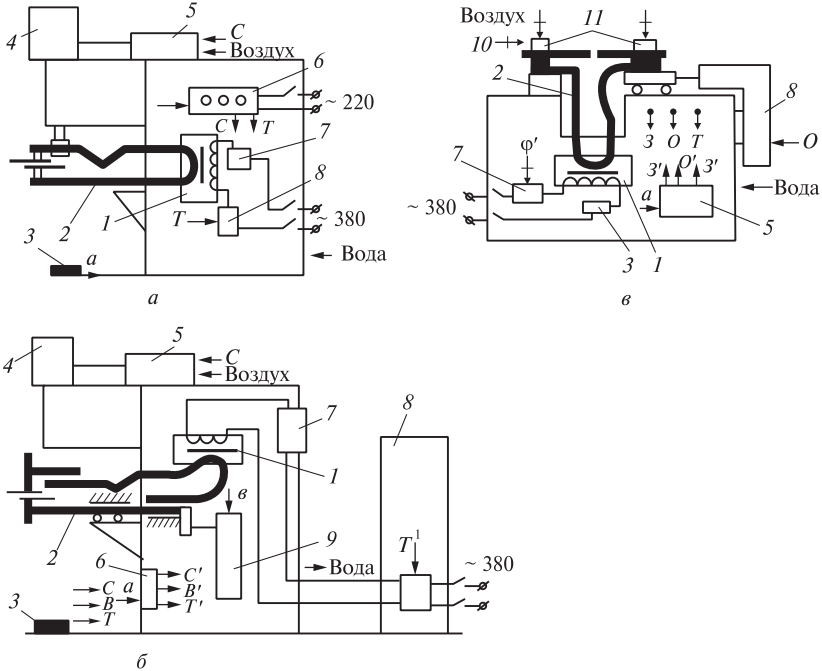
Типовые схемы машин для контактной точечной (а), шовной (б) и стыковой (в) сварки:
